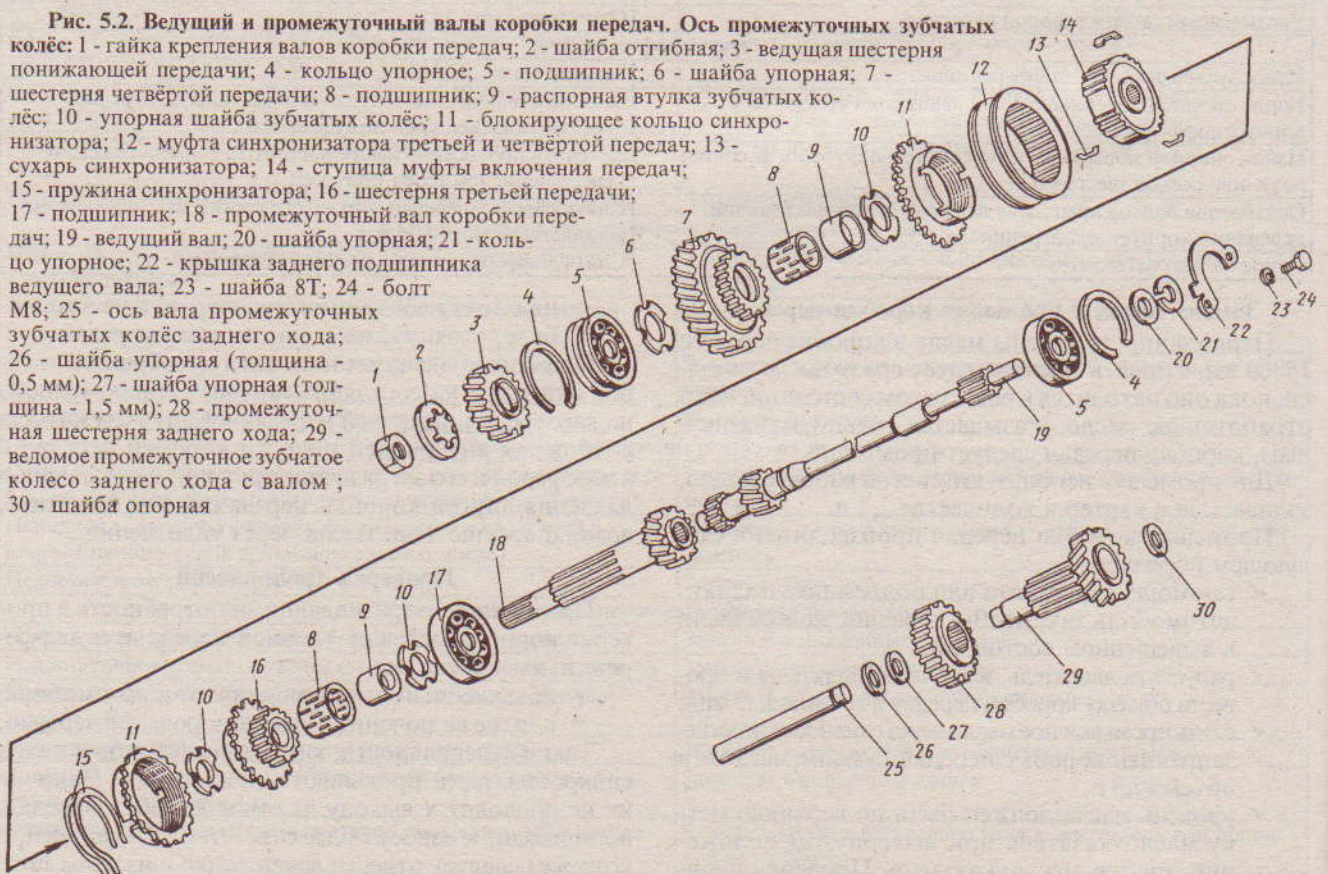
Ведущий и промежуточный валы коробки передач. Ось промежуточных зубчатых колёс: 1 - гайка крепления валов коробки передач; 2 - шайба отгибная; 3 - ведущая шестерня понижающей передачи; 4 - кольцо упорное; 5 - подшипник; 6 - шайба упорная; 7 - шестерня четвёртой передачи; 8 - подшипник; 9 - распорная втулка зубчатых колёс; 10 - упорная шайба зубчатых колёс; 11 - блокирующее кольцо синхронизатора; 12 - муфта синхронизатора третьей и четвёртой передач; 13 - сухарь синхронизатора; 14 - ступица муфты включения передач; 15 - пружина синхронизатора; 16 - шестерня третьей передачи; 17 - подшипник; 18 - промежуточный вал коробки передач; 19 - ведущий вал; 20 - шайба упорная; 21 - кольцо упорное; 22 - крышка заднего подшипника ведущего вала; 23 - шайба 8Т; 24 - болт М8; 25 - ось вала промежуточных зубчатых колёс заднего хода; 26 - шайба упорная (толщина - 0,5 мм); 27 - шайба упорная (толщина - 1,5 мм); 28 - промежуточная шестерня заднего хода; 29 - ведомое промежуточное зубчатое колесо заднего хода с валом; 30 - шайба опорная
